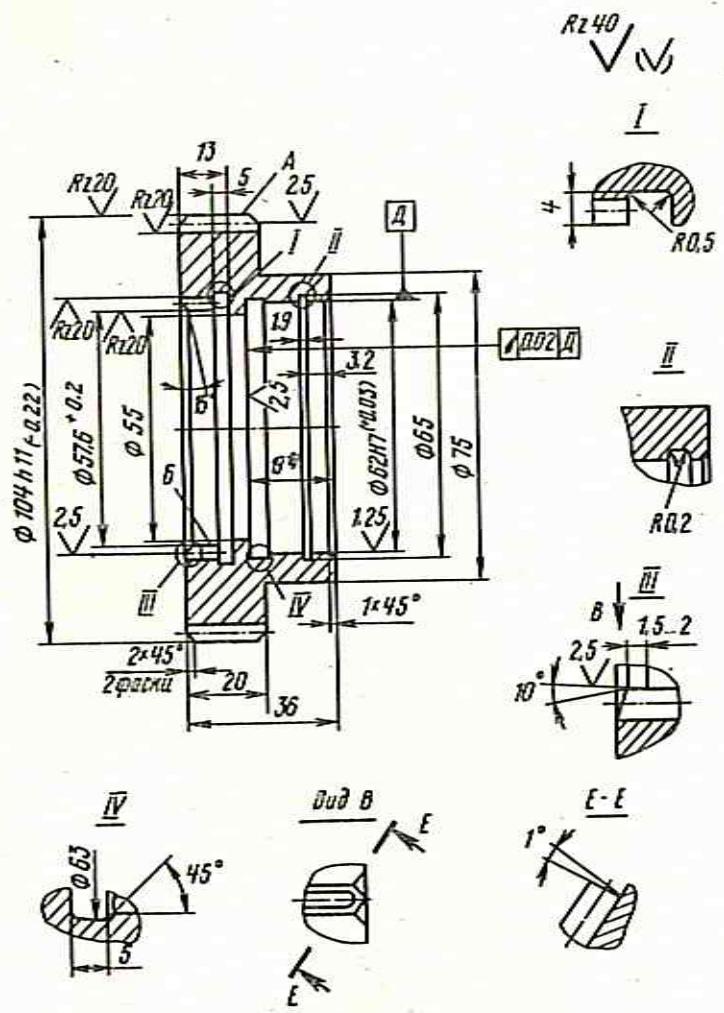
Колесо зубчатое, деталь № ЗЕ722А.322.403
